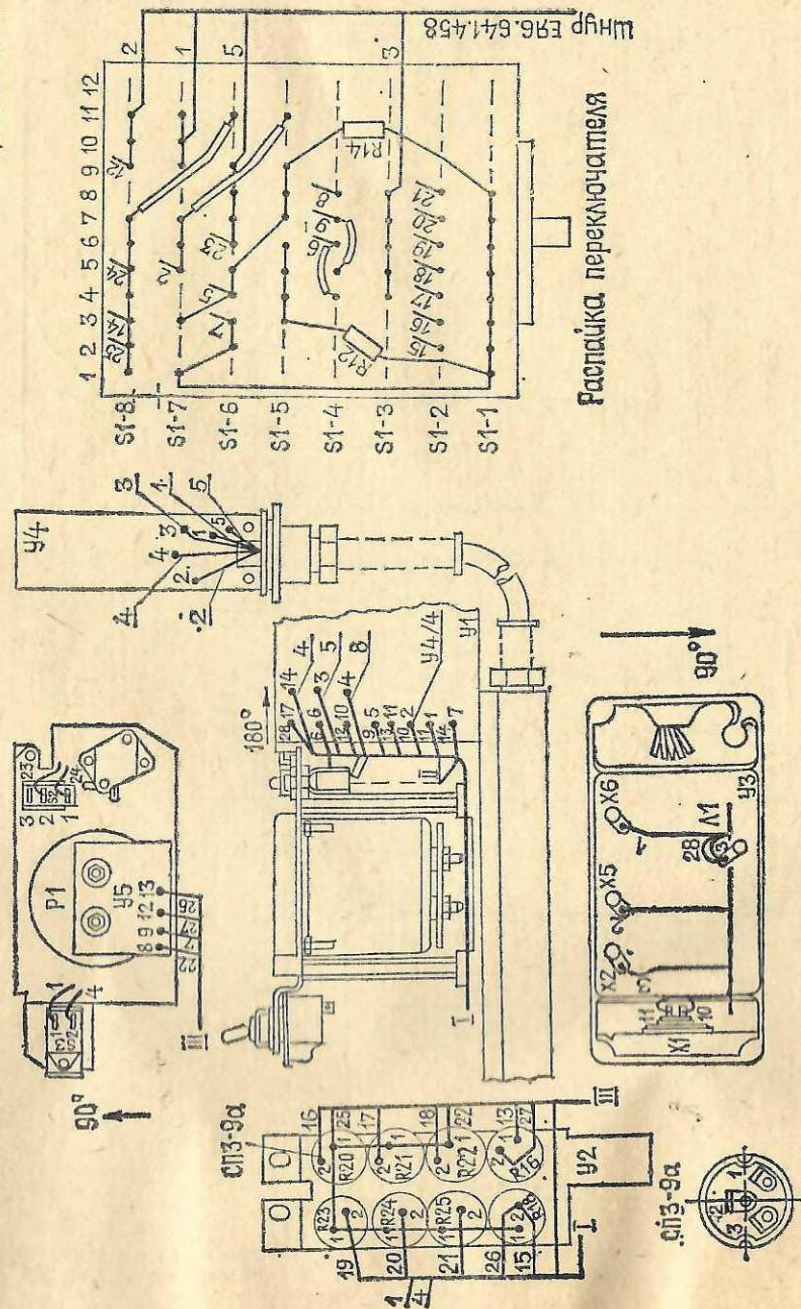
Электромагнитный чертеж прибора ДП-5В.
